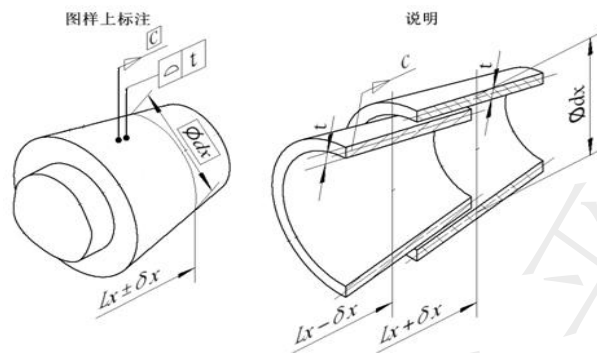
给定圆锥轴向位置公差的圆锥公差注法
